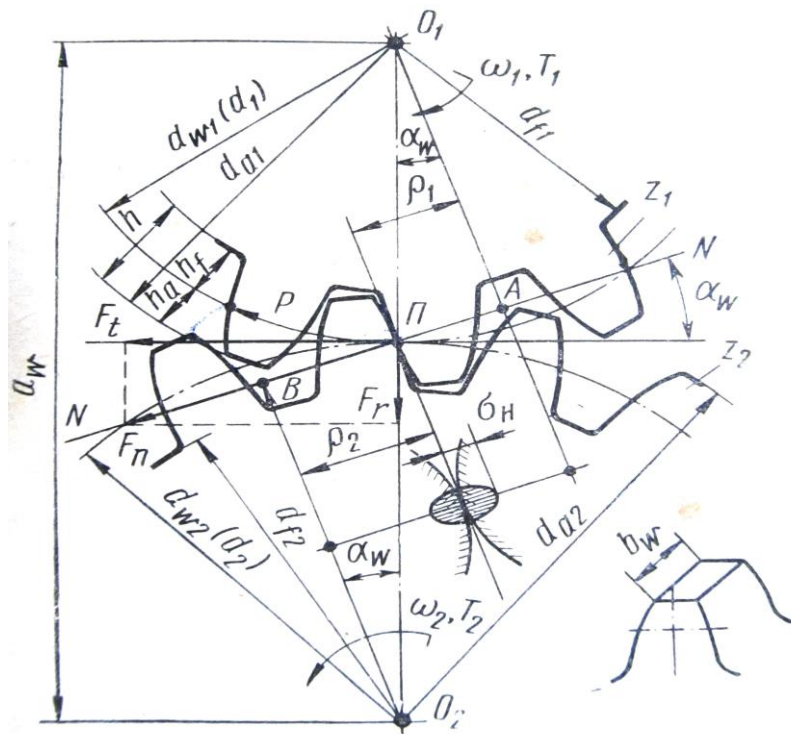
Схема зчеплення двох зубчатих коліс
